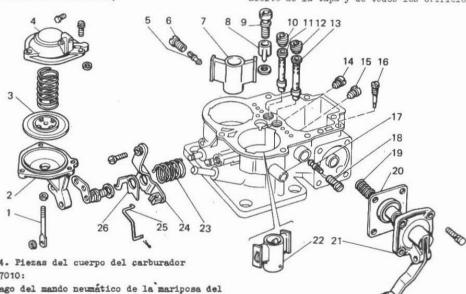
Piezas del cuerpo del carburador 2107-1107010:
